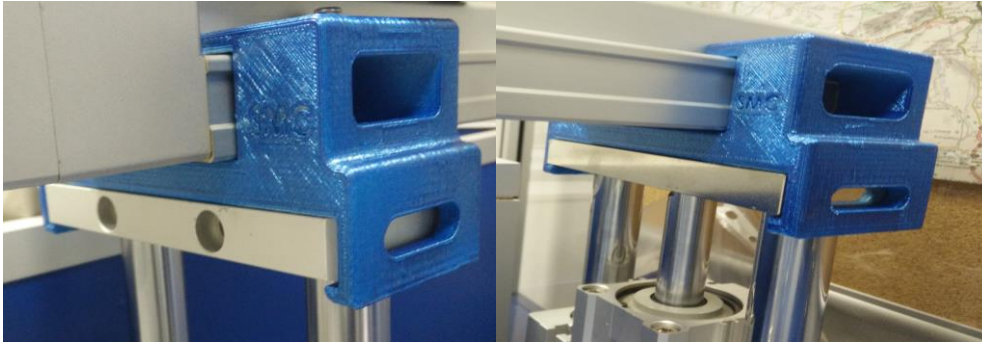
Diseño de la pieza de amarre a la base. A las guías (izquierda) y al cilindro guiado (derecha)
